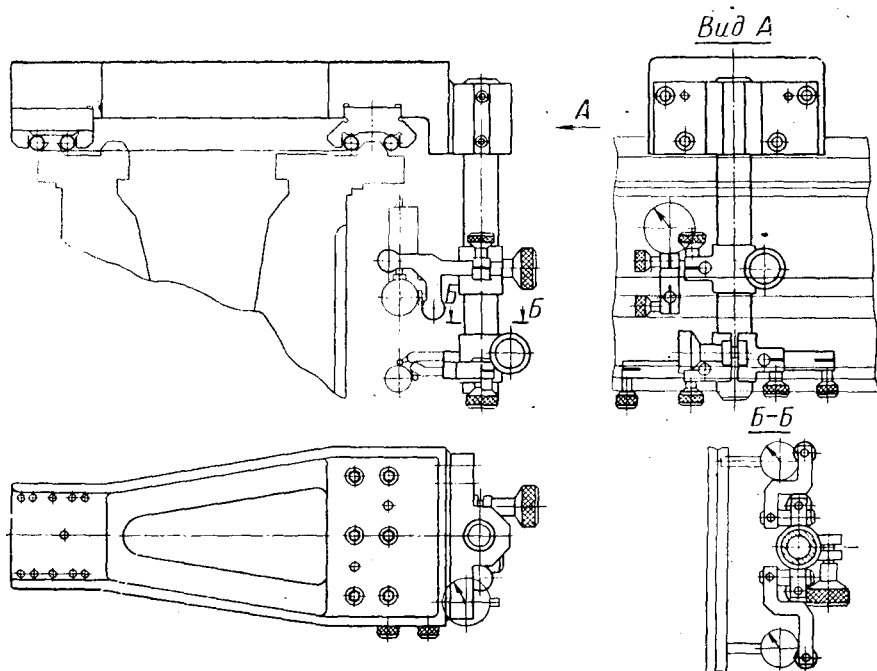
Приспособление для установки ходового винта параллельно направляющим станины
